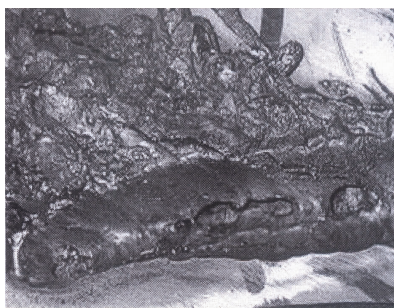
焊缝未熔合缺陷剖面宏观形貌
